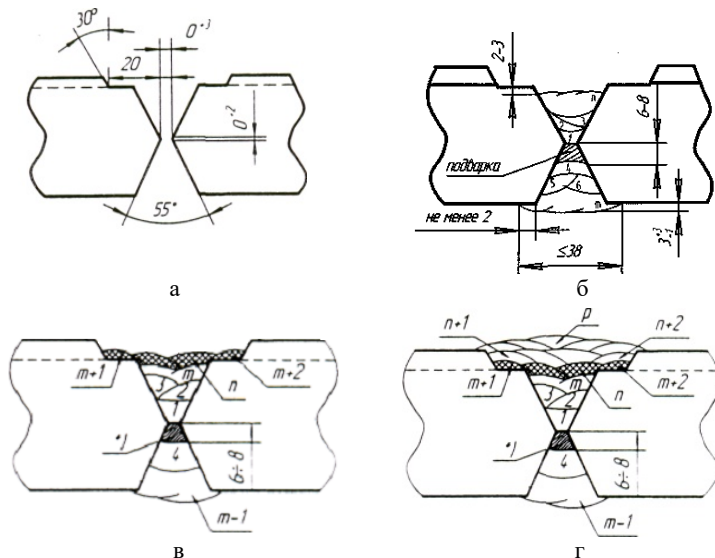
Разделка кромок для сварки плакированной стали 09Г2С+08Х18Н10Т и этапы сварки: а - разделка тип С20 ГОСТ 16098-80; б - сварка основного слоя, стали 09Г2С; в - сварка переходного слоя; г- сварка плакирующего слоя 08Х18Н10Т
